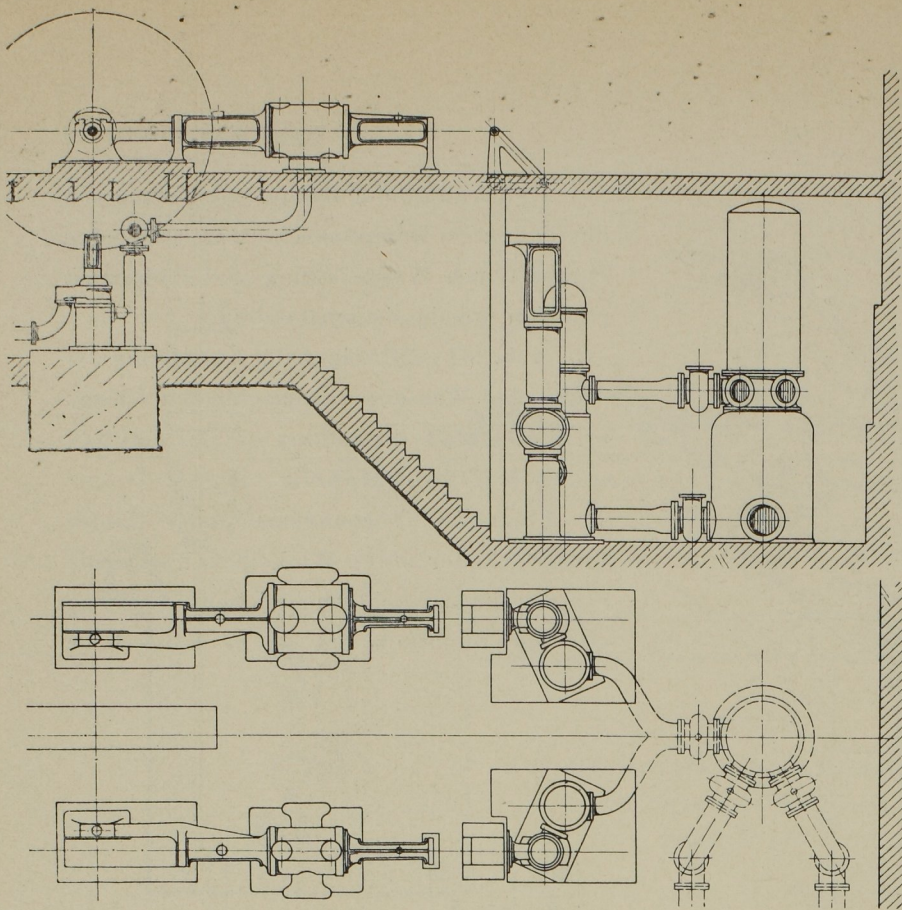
Grundriss und Seitenansicht der Gesamtanlage. Masst. 1 : .00.
